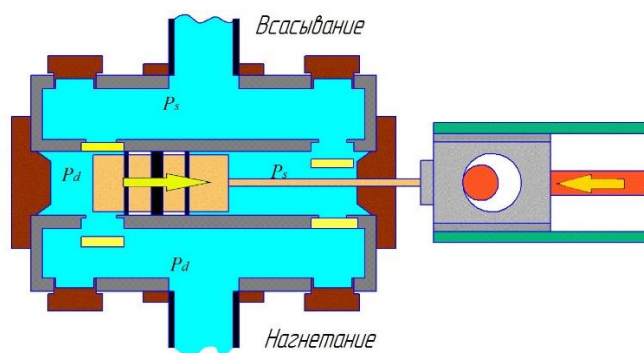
сжатие газа со стороны крышки цилиндра
